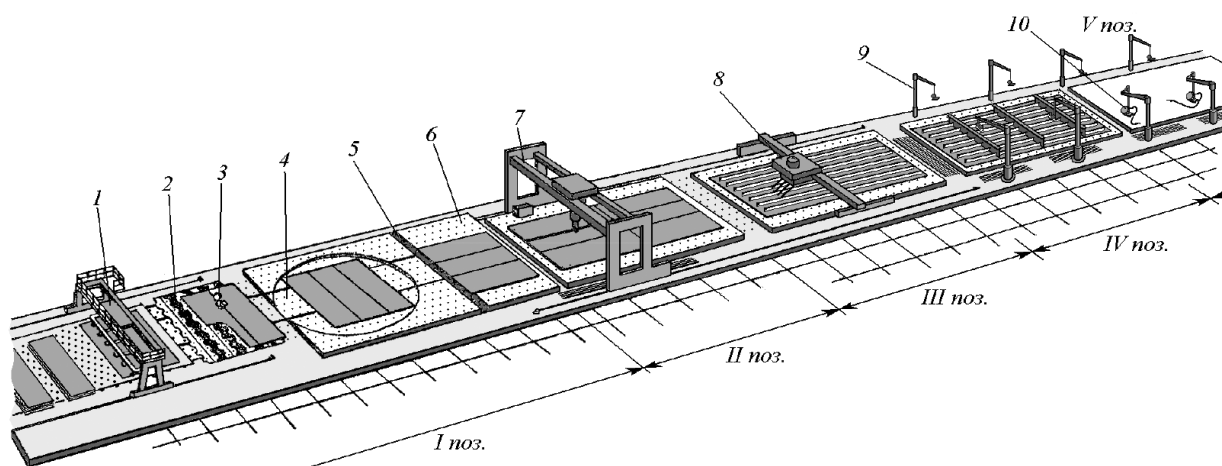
Общий вид механизированной поточной линии для изготовления крупногабаритных плоскостных секций: 1 — листоукладчик; 2 — стенд с синхронным медным ползуном; 3 — автомат сварочный; 4 — разворотный круг; 5 — формирующее устройство; 6 — стенд сборочный с роликоопорами; 7 — перегружатель набора; 8 — агрегат для групповой приварки набора; 9 — грузовая стрела; 10 — сварочная стрела
